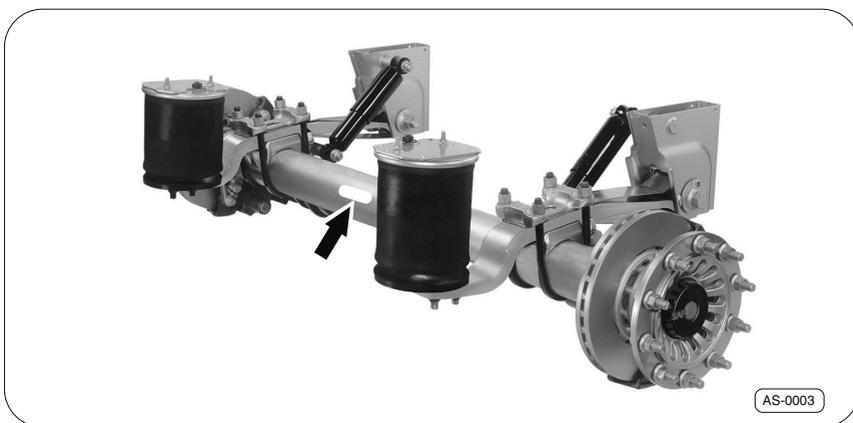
· Position de la plaque signalétique de la suspension pneumatique Type MODUL et essieu livrés sans suspension
